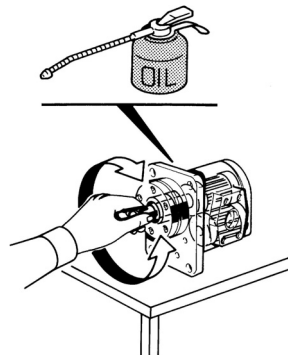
Проверните приводной вал вручную. Затем подайте в шестеренчатый насос масло, для того чтобы предварительно смазать подшипники скольжения и зубчатое зацепление
